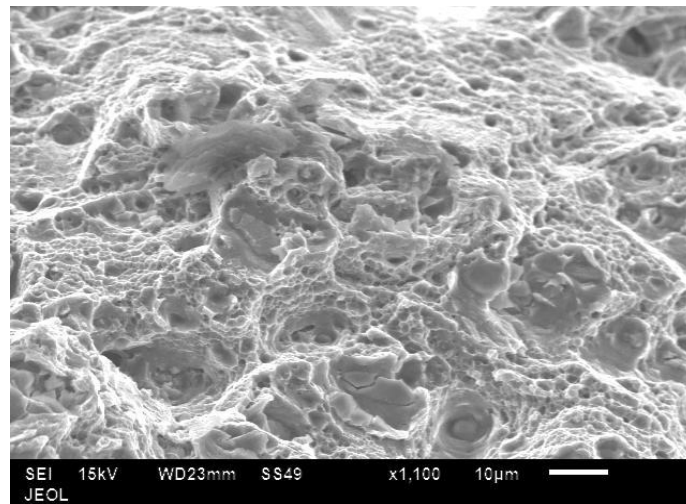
Analyse fractographique à 30mm de l'entaille pour une éprouvette réparée sous L-H blocs à 1x 20
